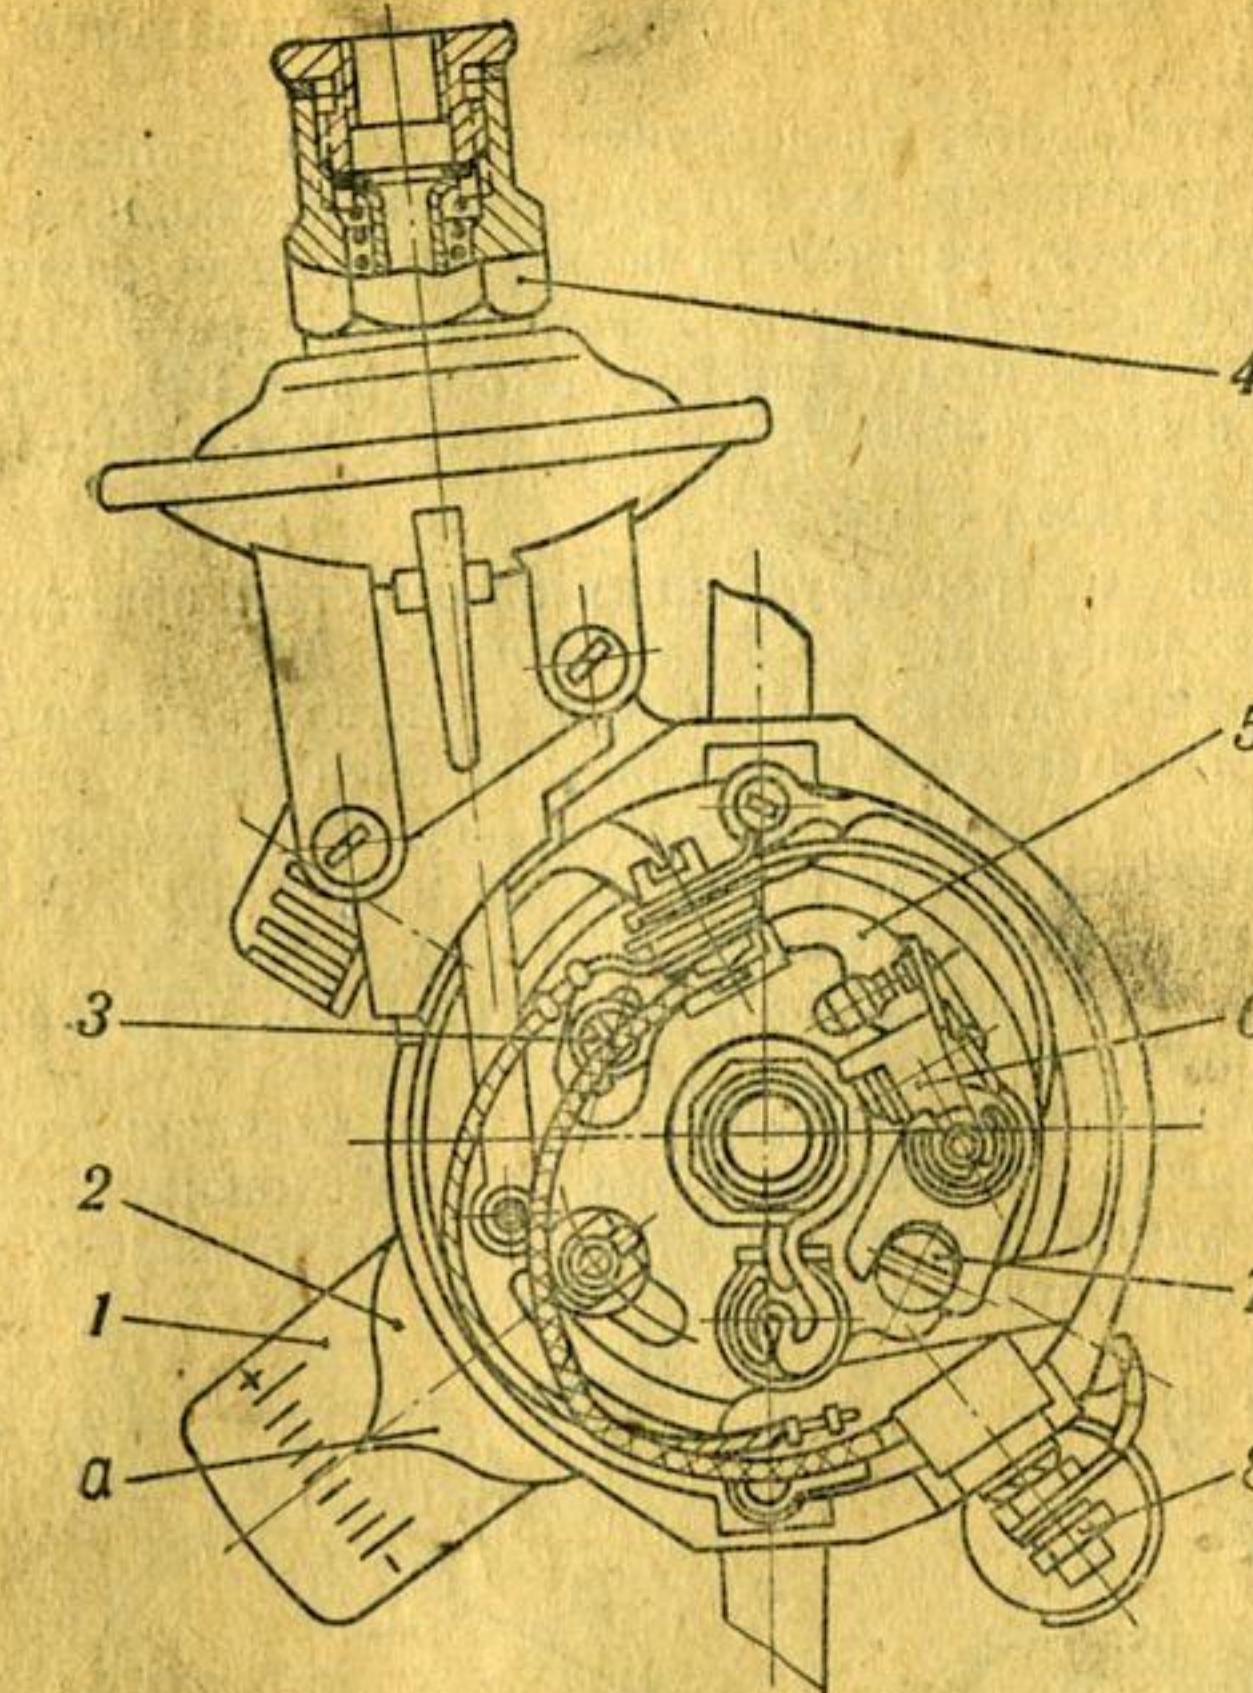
Распределитель зажигания типа Р118 со снятой крышкой и ротором:
